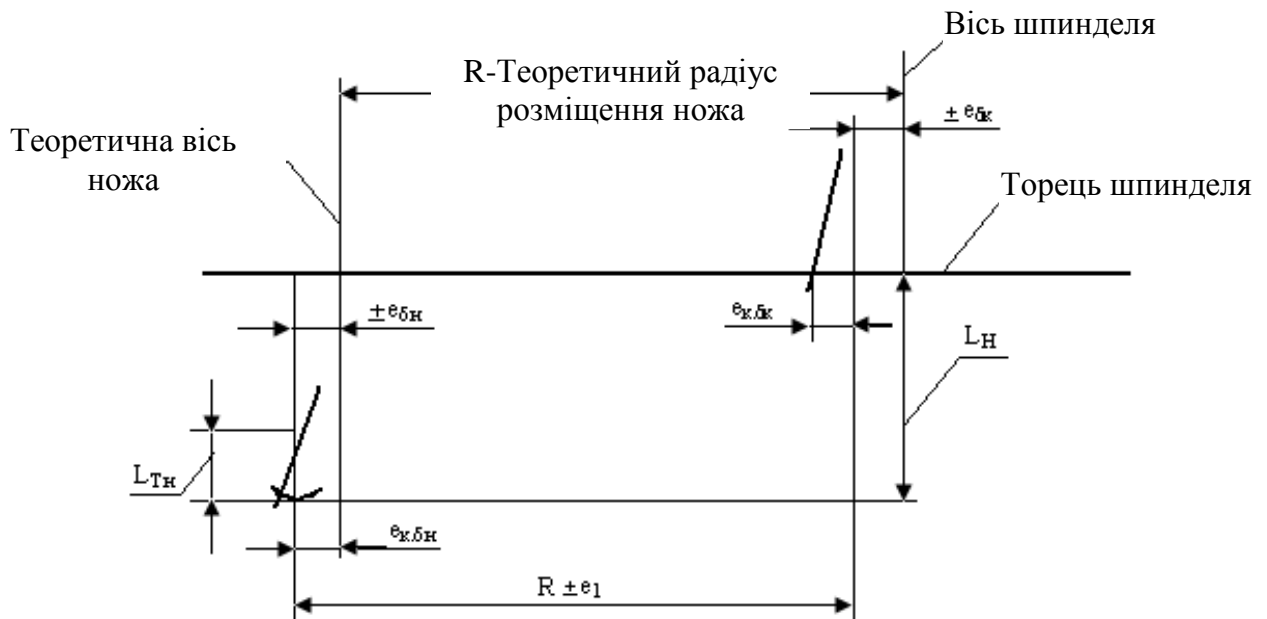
Схема виникнень відхилень розташування вершини ножа щодо його теоретичного положення:
